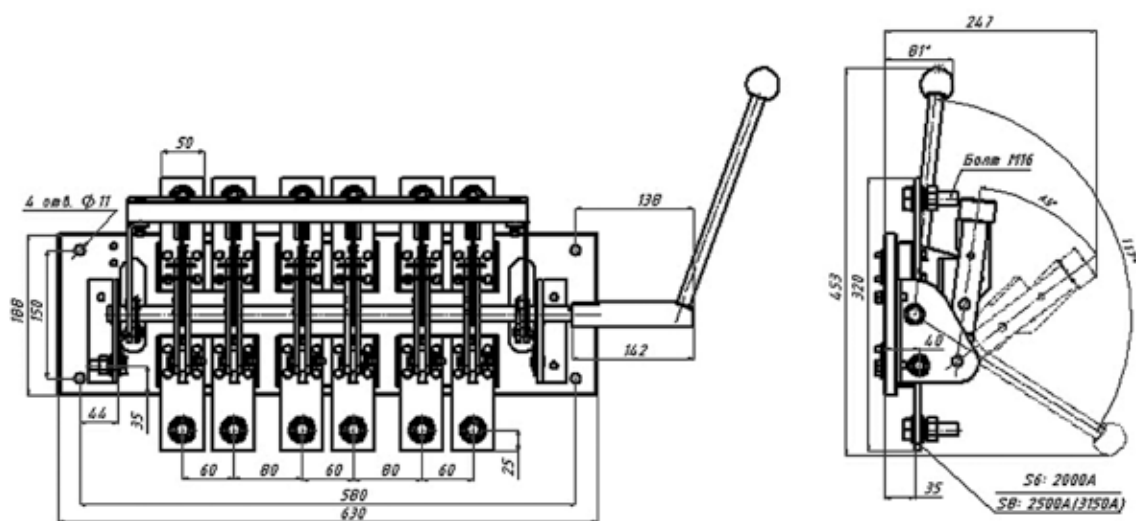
Разъединитель PE19 с боковой смещенной рукояткой PE19-44(45; 46)-31150-00 УХЛЗ
